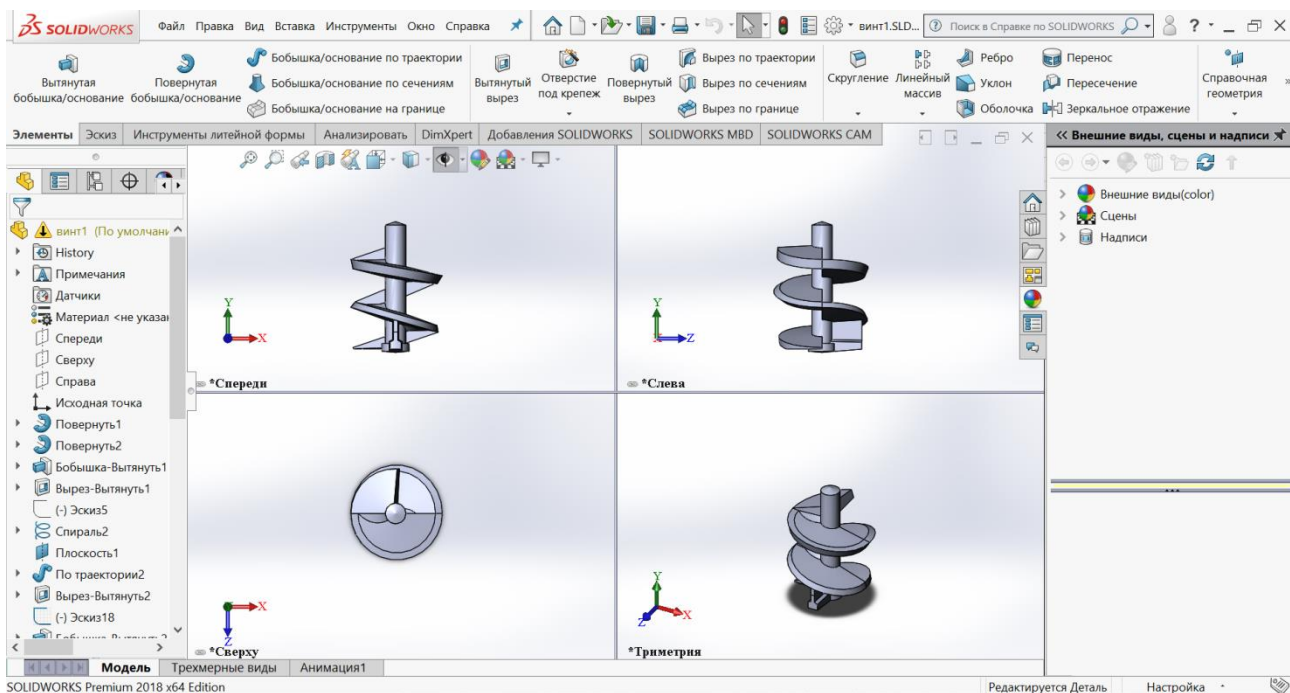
3D модель отливки детали – “Винт” термической печи отжига
